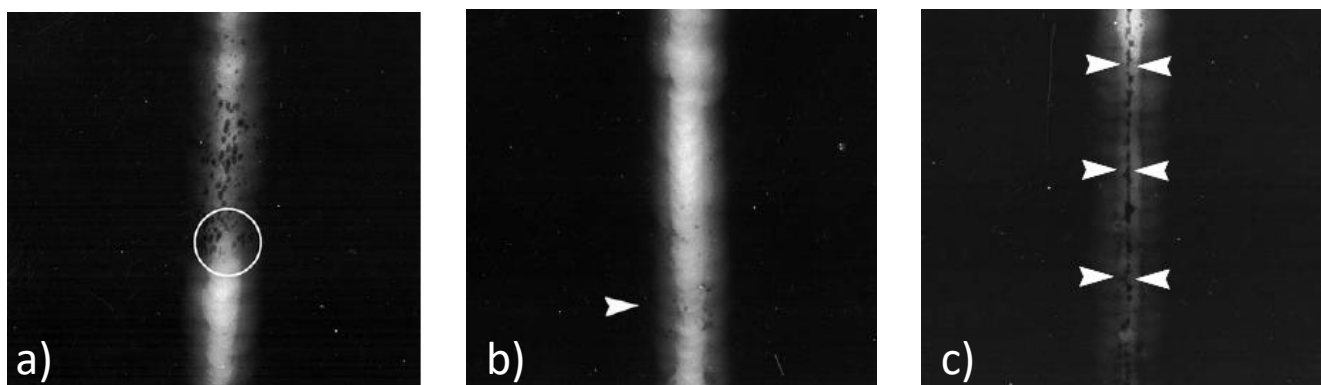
Imágenes radiográficas de tipos de porosidad en cordones de soldadura a) agrupada b) dispersa c) lineal [3].
